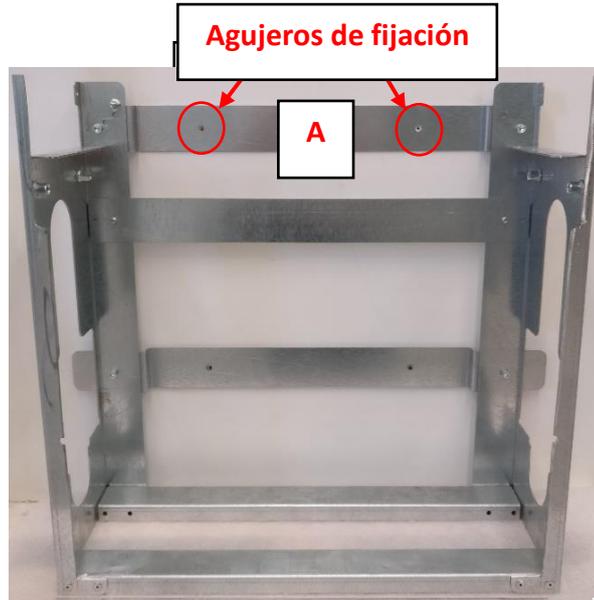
Montaje en la pared de la caja de baterías WALL-BOX-BxBASE
